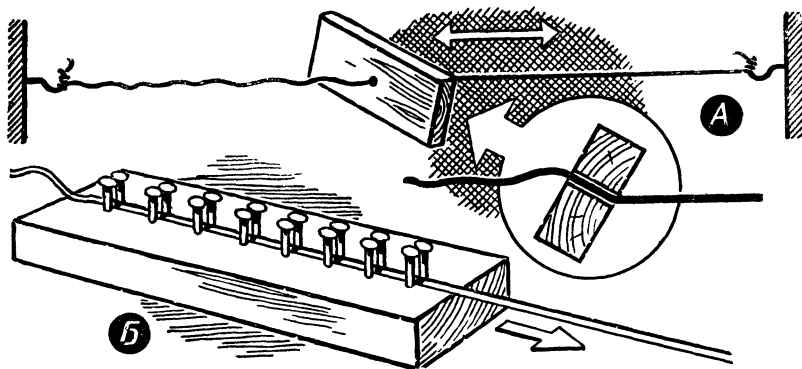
Рихтовочные приспособления: А — фанерка с отверстием; Б — доска с набитыми гвоздями.
